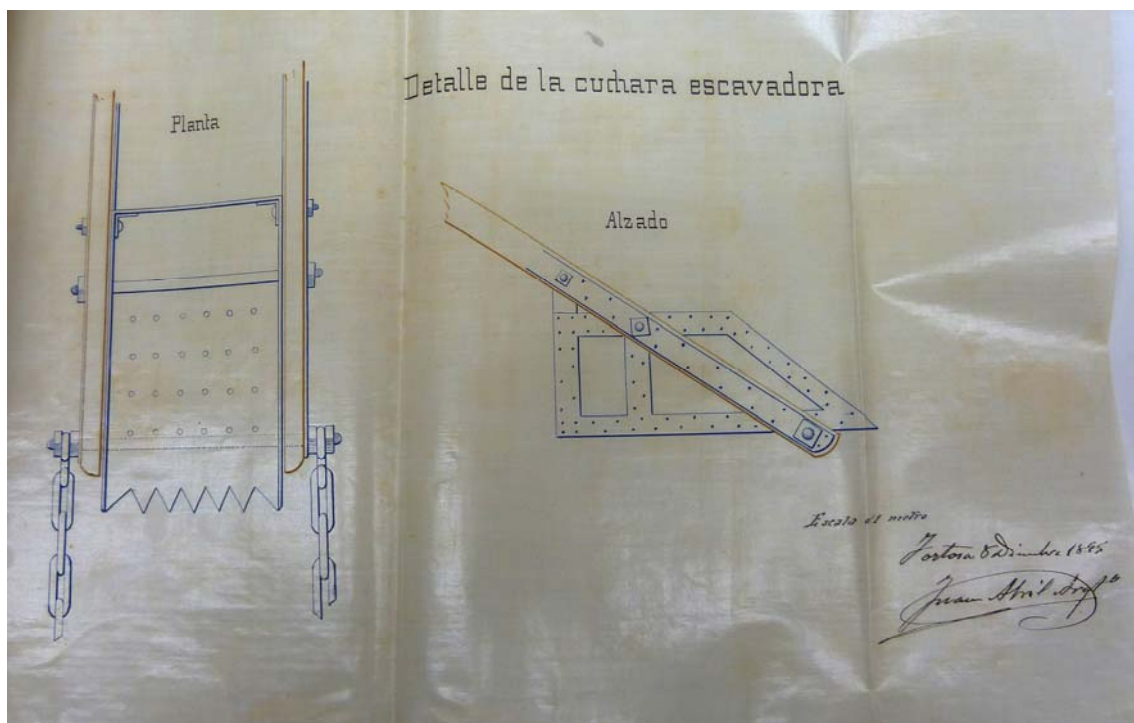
Proyecto de restauración de Abril i Guanyabens: Dibujo de las máquinas previstas para ejecutar la obra.
